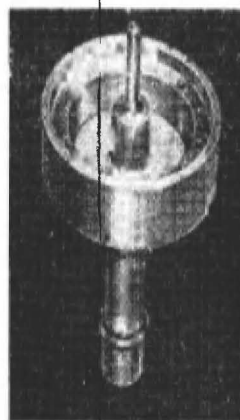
Общий вид узла ведущего вала магнитофона «Гинтарас».
